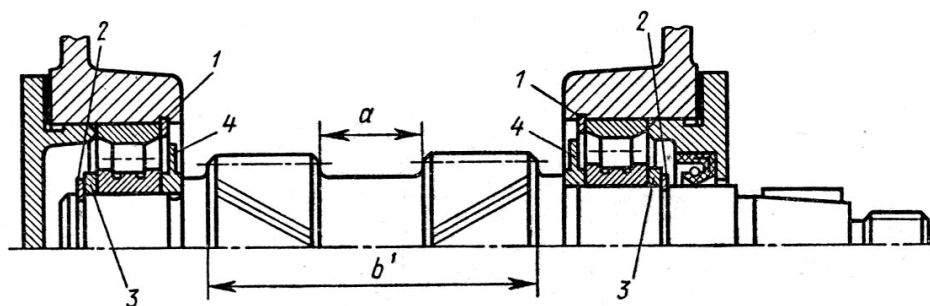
Опоры вала шевронного зубчатого колеса
